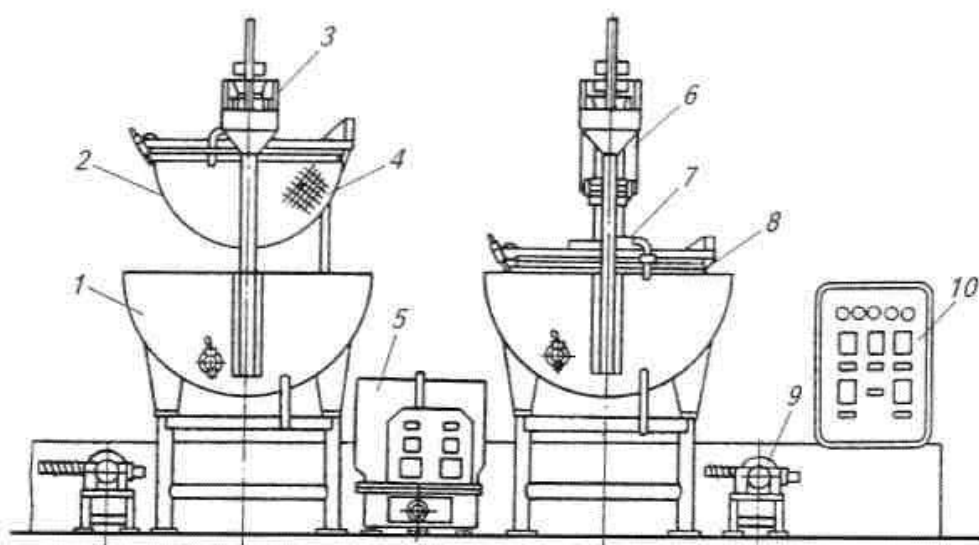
Творогоизготовитель с прессующими ваннами: 1 — нижняя ванна для сквашивания молока; 2 — прессующая перфорированная ванна; 3 - траверса; 4 — стойка; 5 — гидропривод; 6 — гидроцилиндр; 7—плита; 8 — поворотный упор; 9 —насос для откачивания сыворотки; 10 — пульт управления
